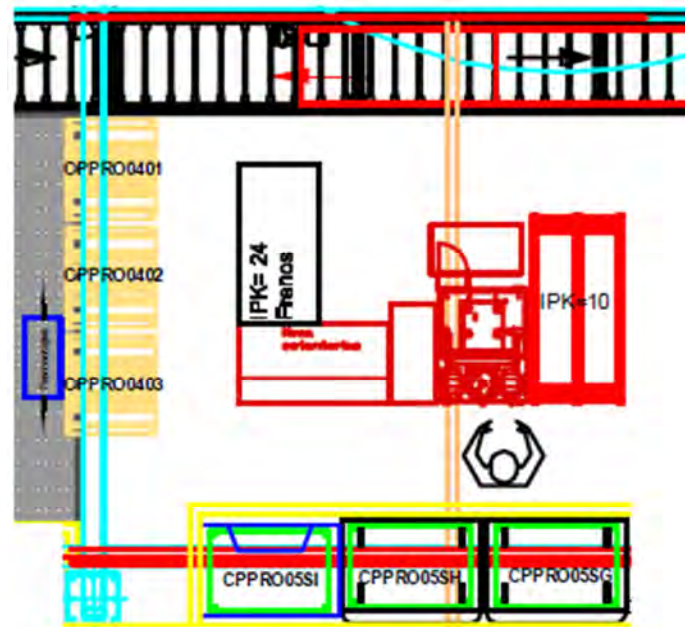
K LAYOUT PUESTO DE PREMONTAJE DEL FRENO DE SERVICIO
